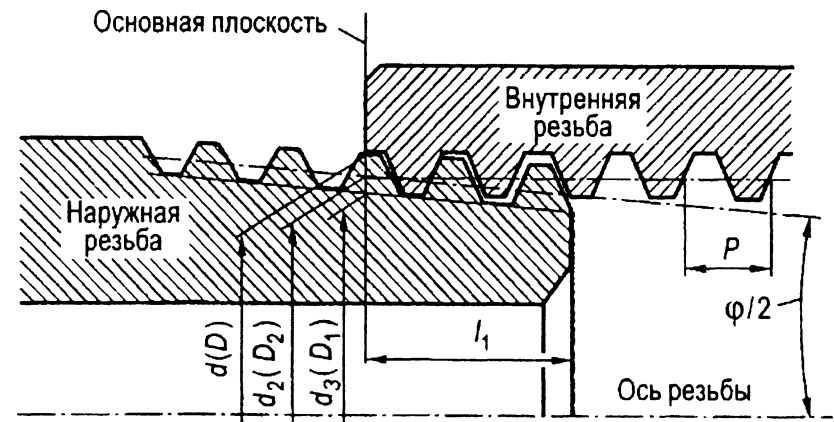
Соединение наружной конической резьбы с внутренней цилиндрической резьбой
